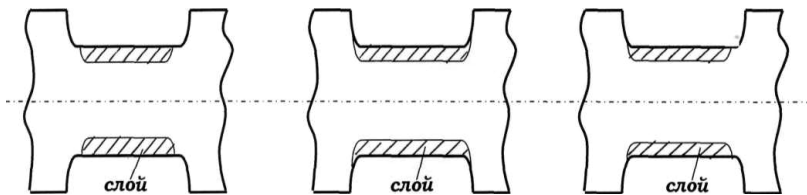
Схема расположения закаленного слоя по шейке коленчатого вала
